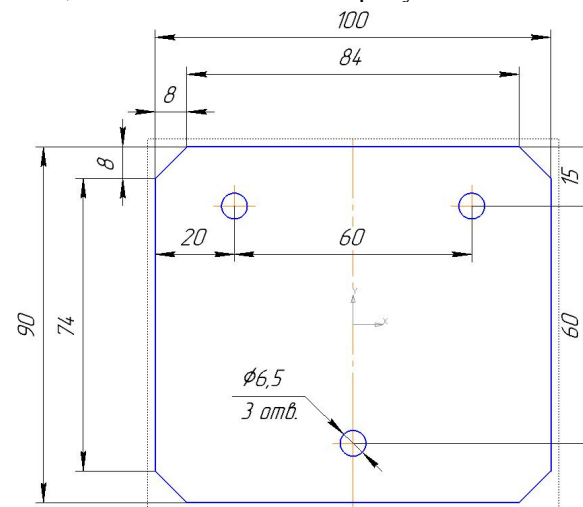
Общий вид и присоединительные размеры монтажного кронштейна
